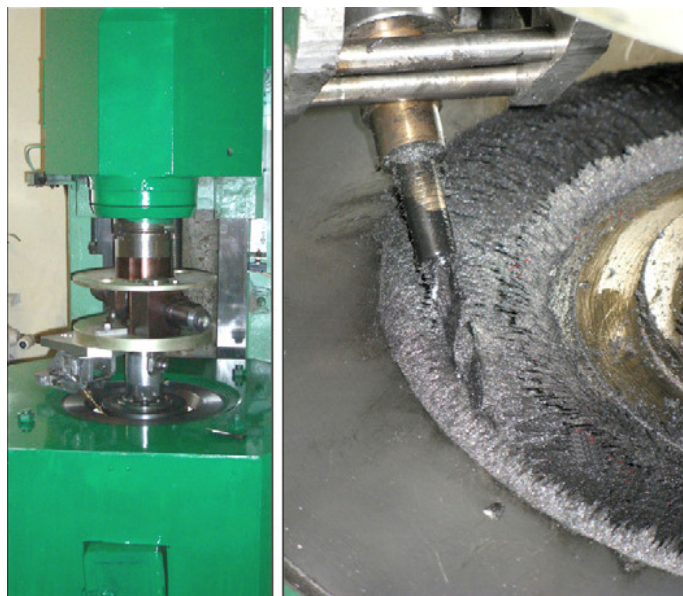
Demonstração da máquina no teste de usinagem [32]
